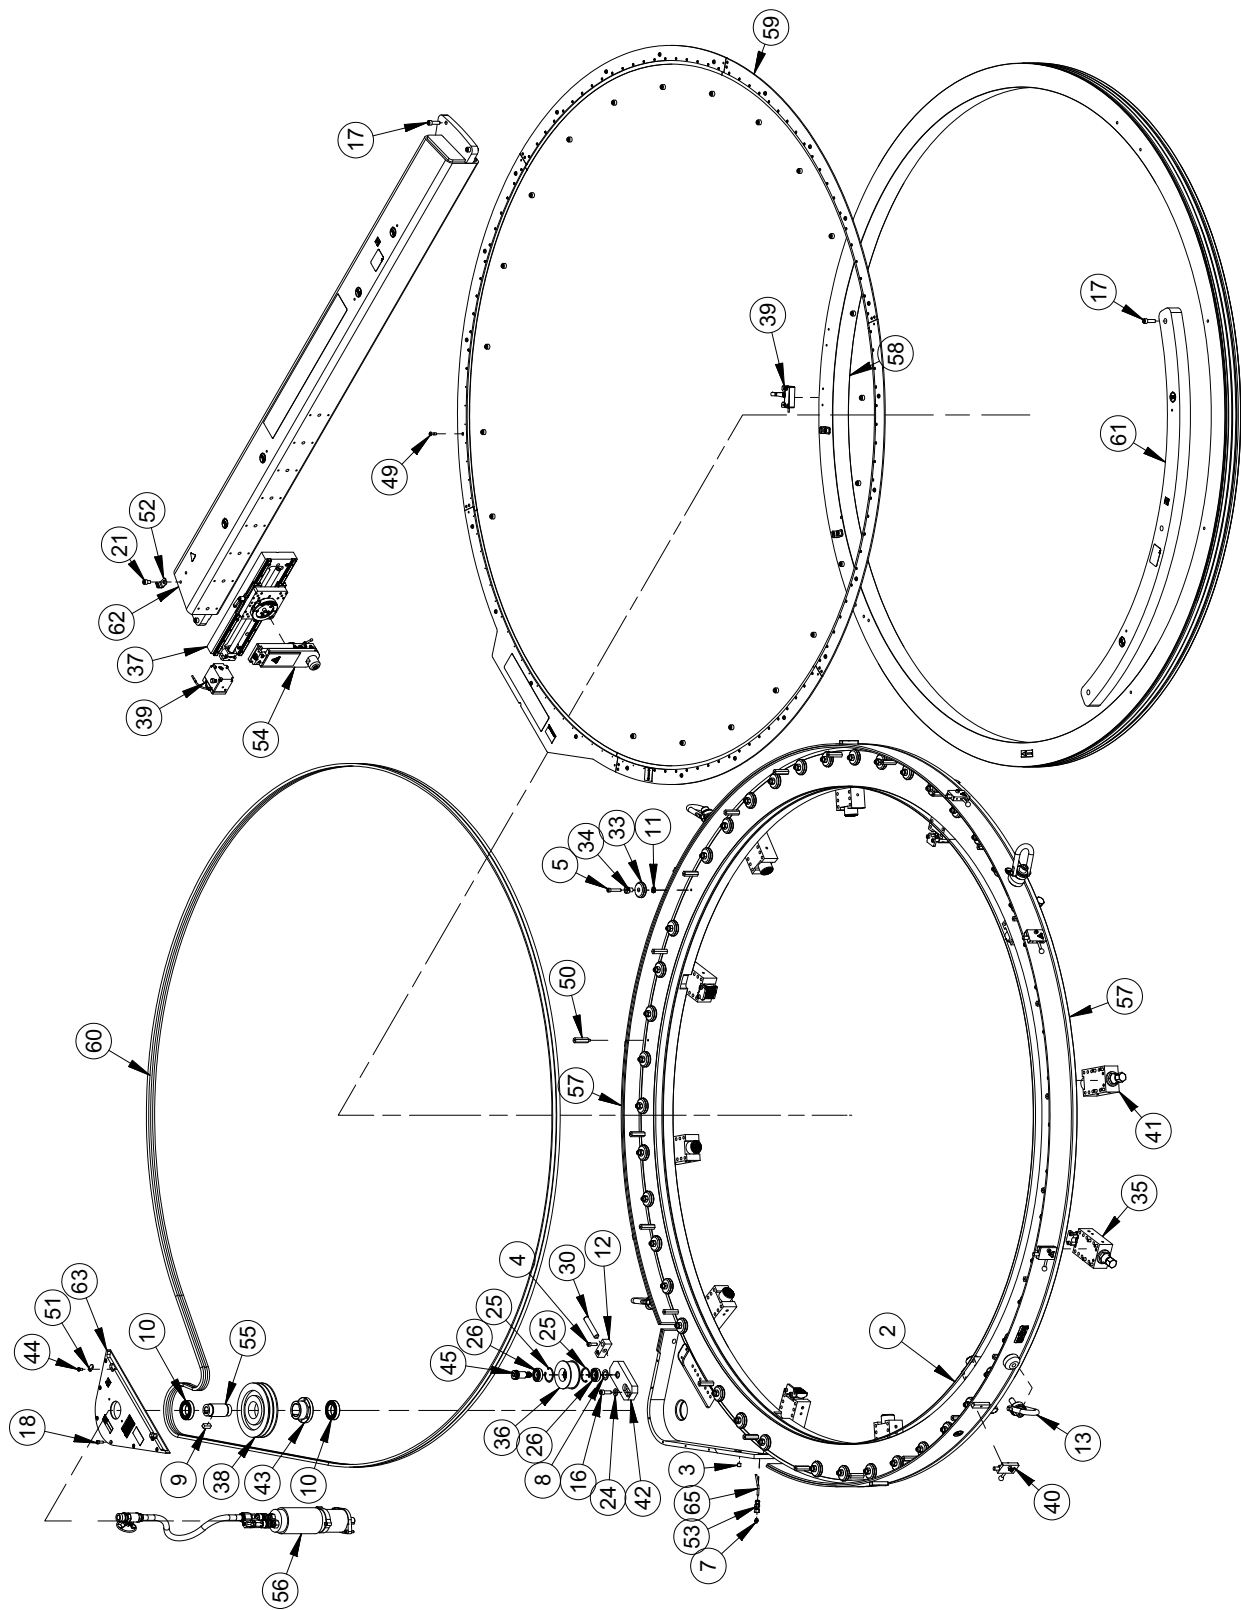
CONJUNTO 1 DE ODF100 SPEED FACER (N/P 94790)
